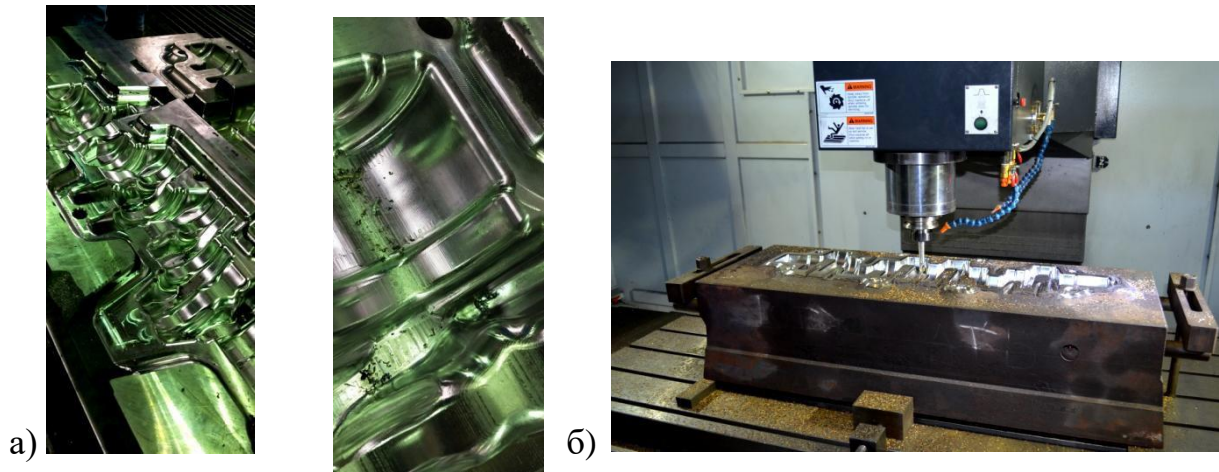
а) Поверхности гравюры штампа горячей объемной штамповки коленчатого вала после чистового фрезерования, б) процесс фрезерования гравюр штампа вставки на фрезерном станке с ЧПУ
